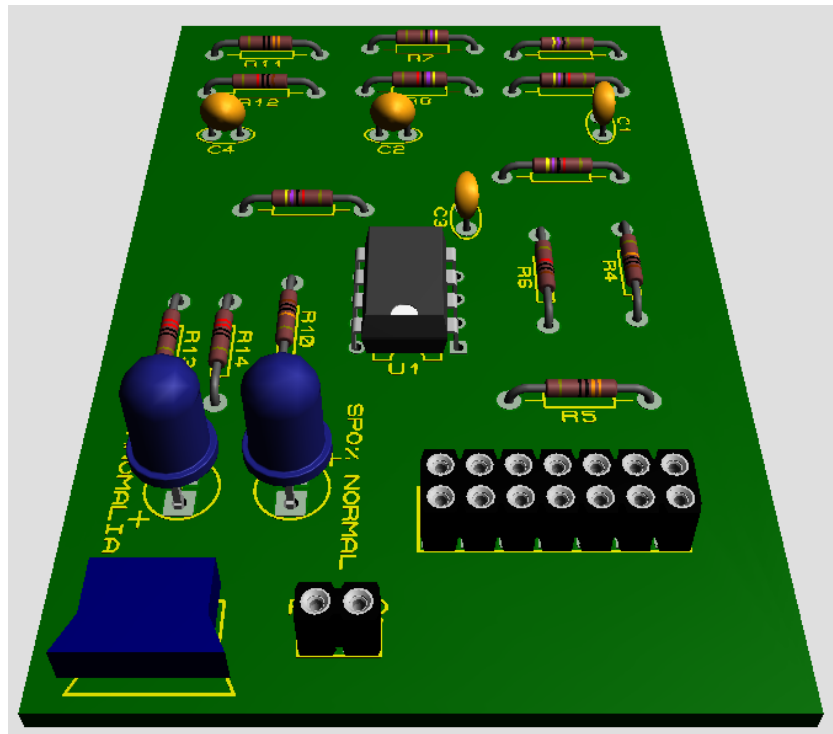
Vista Derecha de Circuito en Placa PCB
